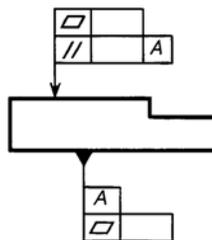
Обозначение двух разных видов допуска
